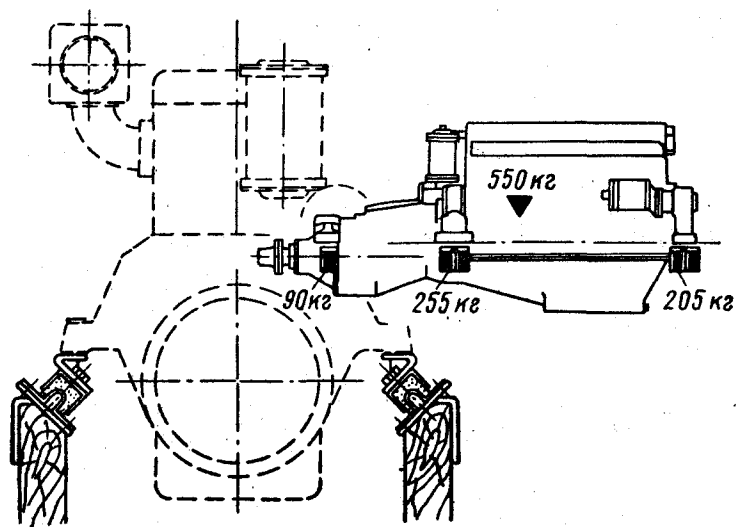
Эластичное крепление катерного двигателя с использованием блоков-амортизаторов с резинометаллическими прокладками. Слева — контур двигателя с наклонным креплением блоков. Справа — установка на пяти резинометаллических блоках с каждой стороны двигателя с указанием распределения нагрузки.
